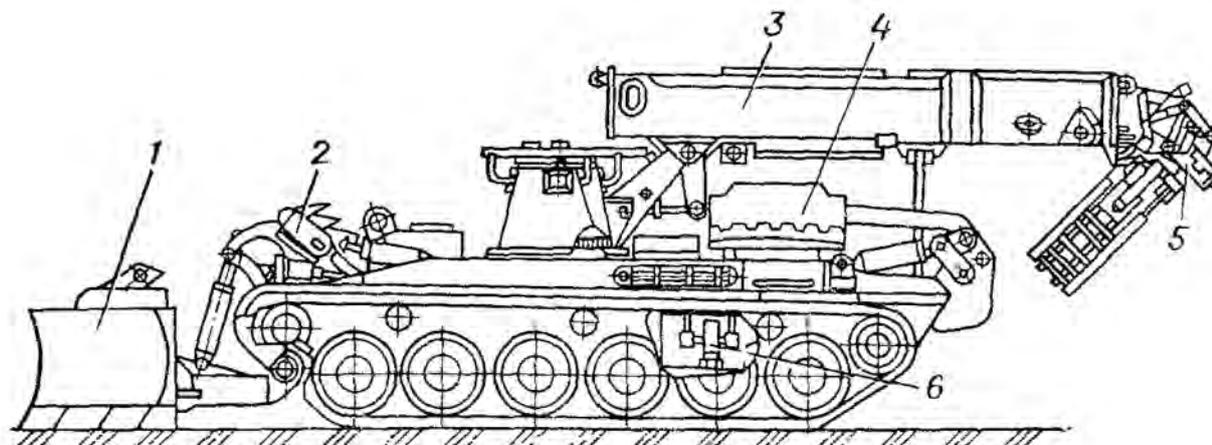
Рабочее оборудование машины ИМР-2М: 1 — бульдозер универсальный; 2 — ножевой колеяный минный трал; 3 — полноповоротная телескопическая стрела; 4 — скребок рыхлителя; 5 — манипулятор; 6 — редуктор насосов гидропривода
